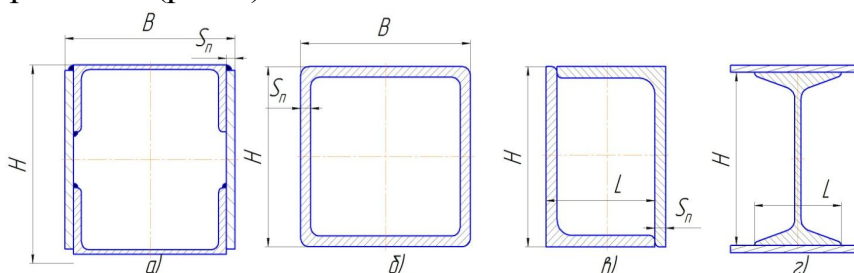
Металлоконструкции, применяемые в СДМ: а - балка с усиливающими пластинами выполненная из 2-х швеллеров; б - балка коробчатого сечения; в - балка выполненная из 2-х уголков; г – двутавр с усиливающими пластинами.
